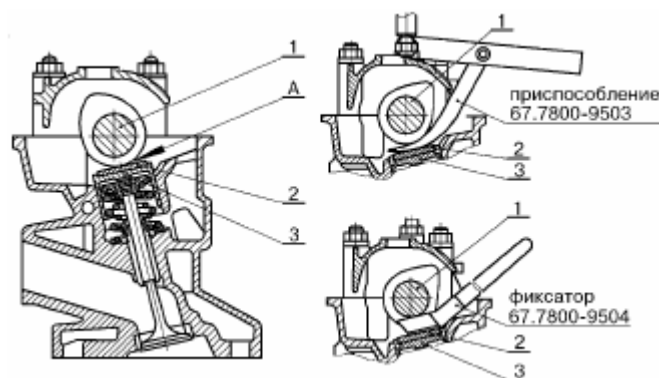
Схема перевірки зазору в механізмі приводу клапана
